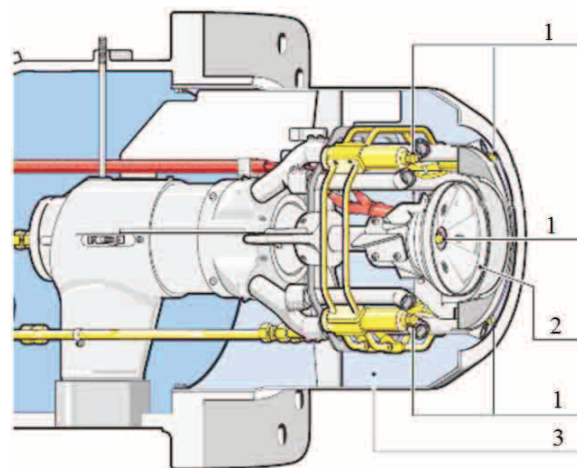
Конструктивная схема исследуемой горелки [25]: 1 – форсунки подачи синтез-газа; 2 – каналы подачи первичного воздуха; 3 – канал подачи вторичного воздуха
